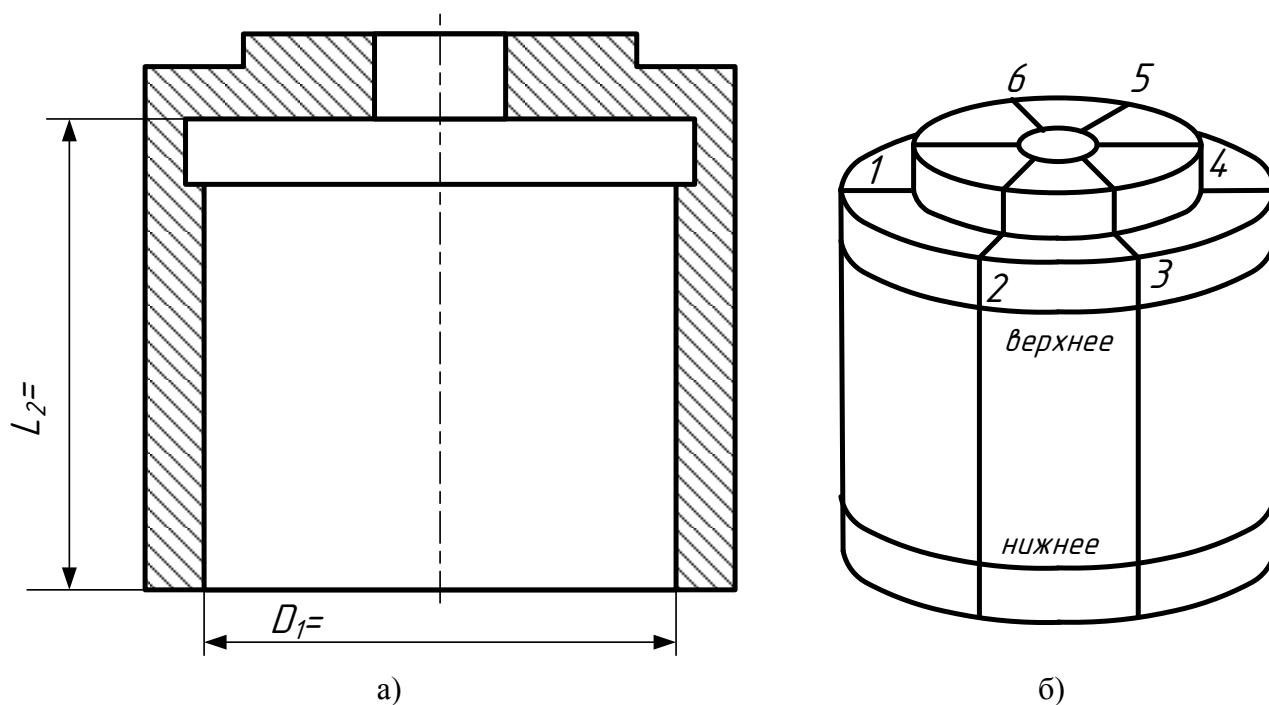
Эскиз измеряемой детали № ____ и схема разбивки детали на сектора
